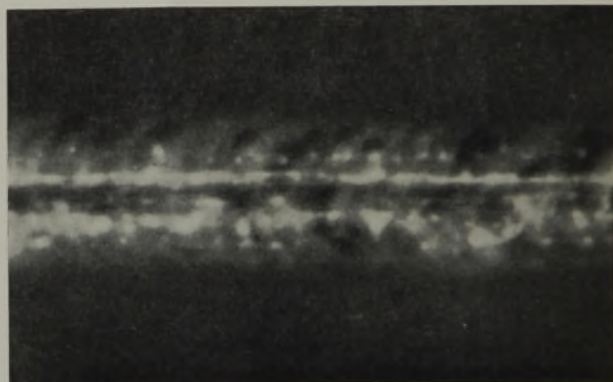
Beispiel einer schlecht ausgeführten Schweißnaht.
